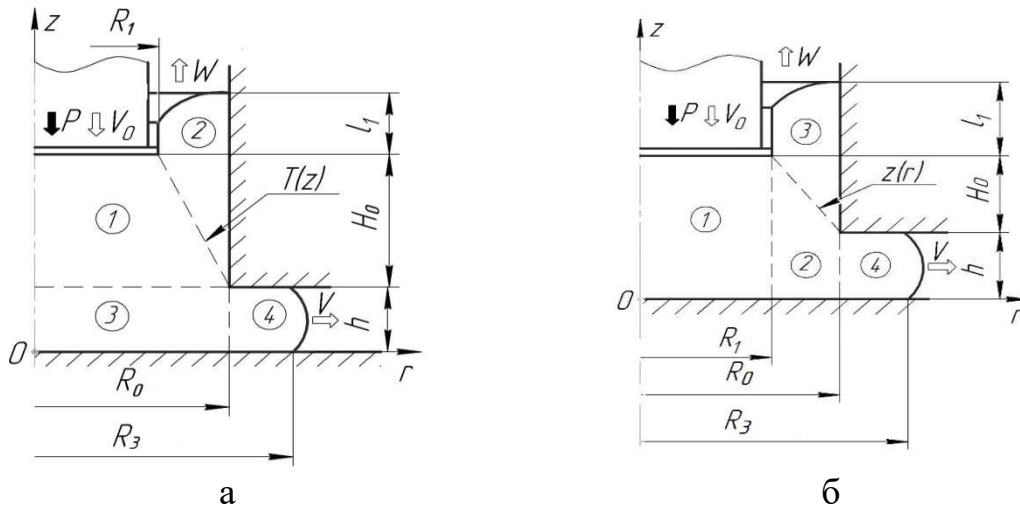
Розрахункові схеми процесу комбінованого видавлювання порожнистих деталей з фланцем
